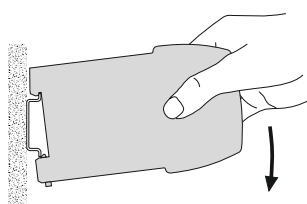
Montage sur rail «à chapeau» 35 15 ou 35 7,5 mm.
